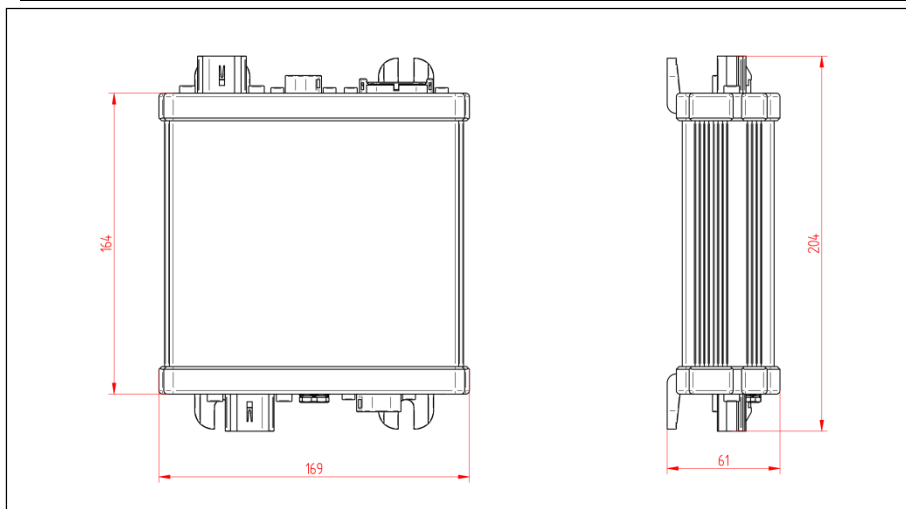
размеры ECU Двигатель код 10CEN-0003.
